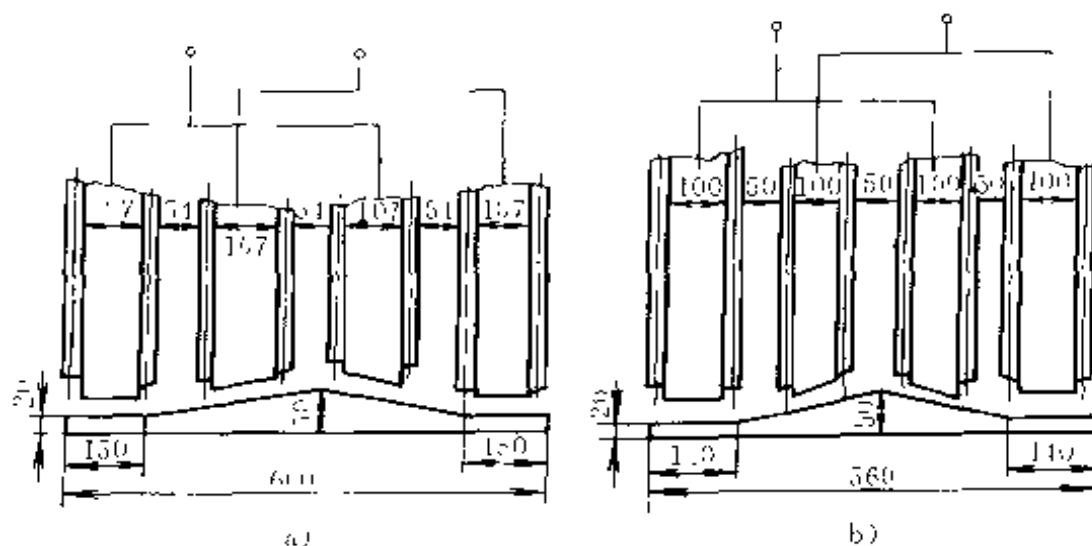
立辊轧机机架电渣焊熔嘴排列尺寸及引弧板尺寸
